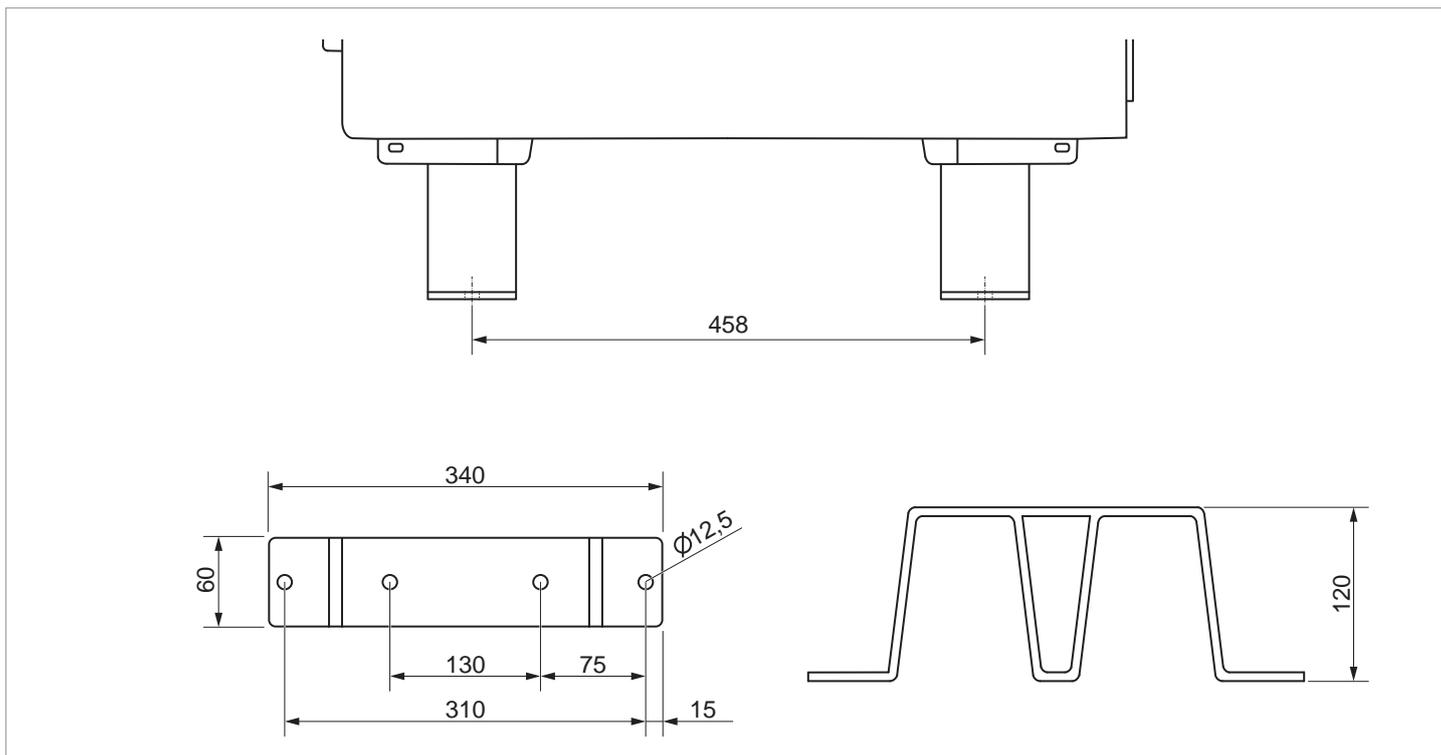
Pieds pour montage au sol. Dimensions (données en mm)
